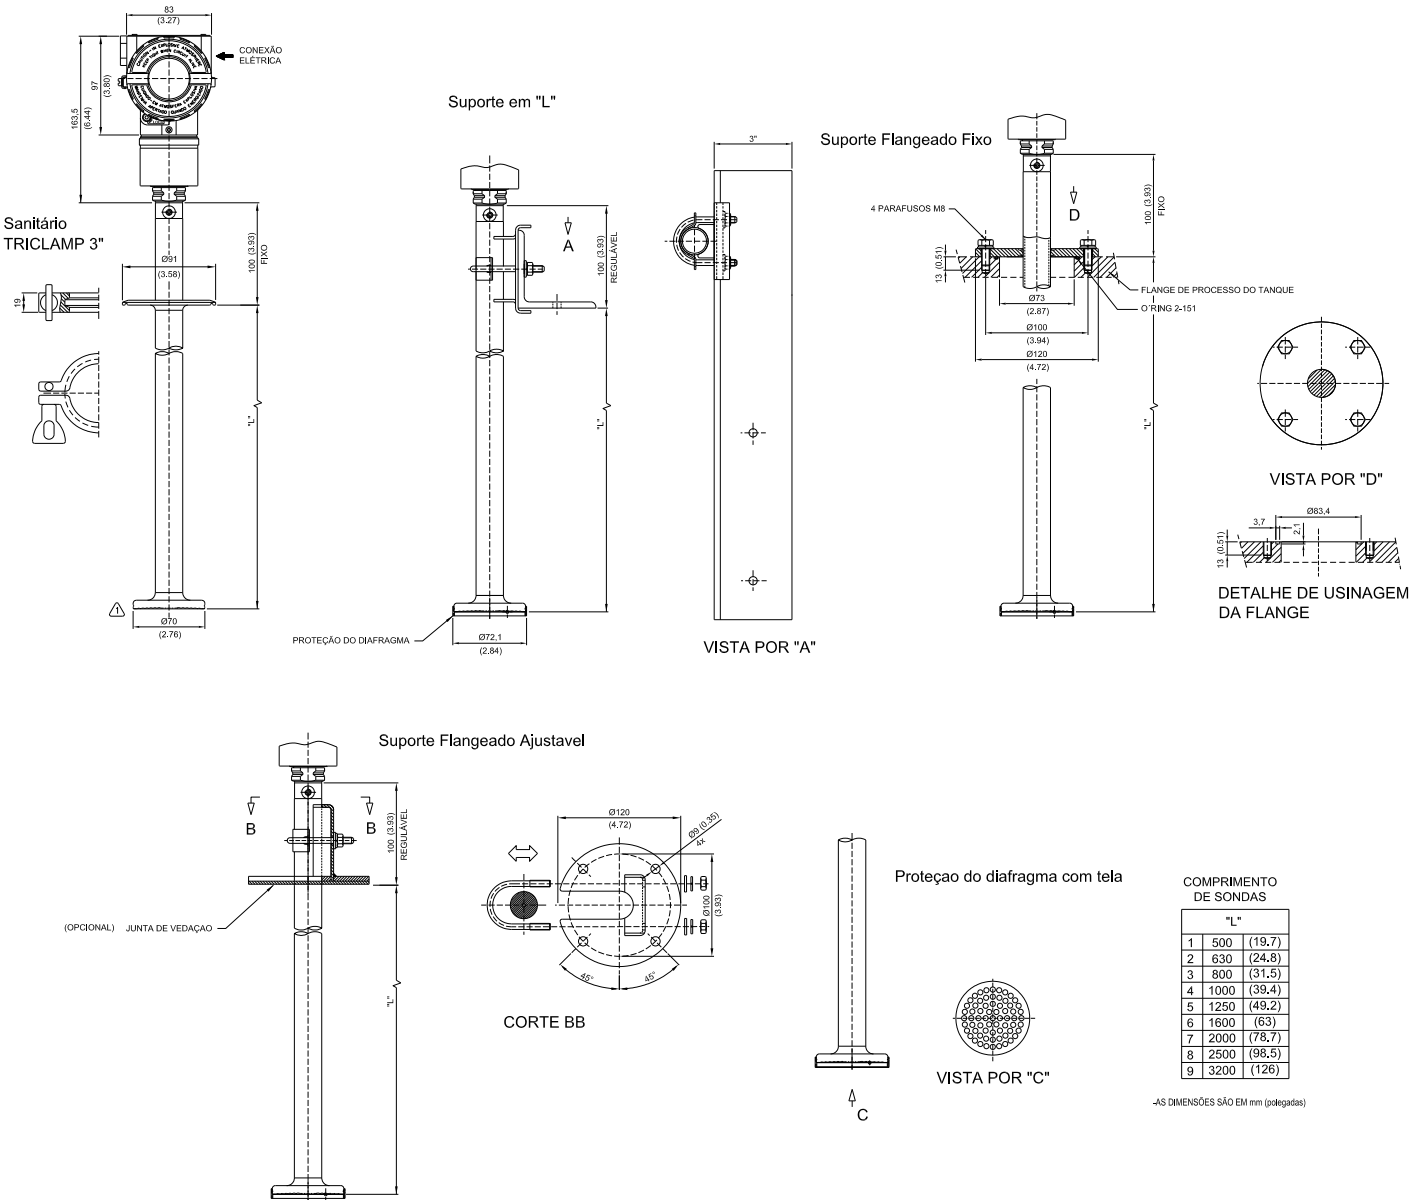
(e)– Desenho Dimensional e Posição de Montagem para o LD293 – Transmissor de Nível (Inserção)
